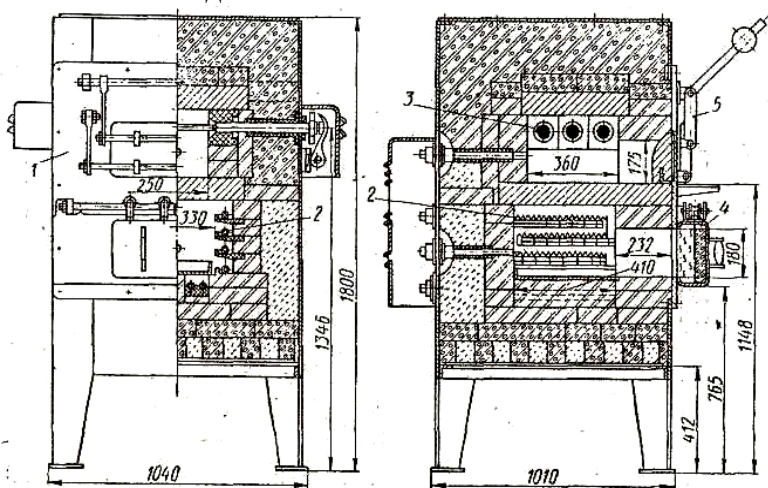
Двокамерна електропеч для обробки швидкорізальної та високохромистої сталі: 1 - кожух печі; 2 - нагрівачі нижньої камери; 3 - нагрівачі верхньої камери; 4 - дверцята нижньої камери; 5 - механізм підйому дверцят верхньої камери
